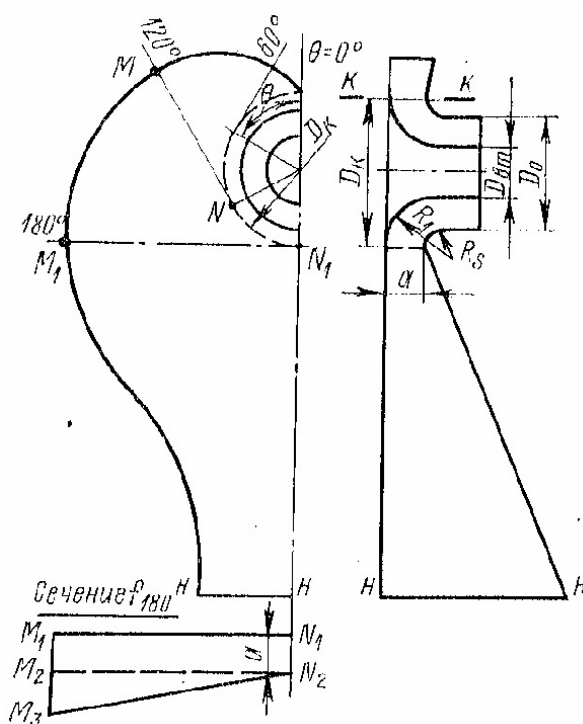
Схема и основные размеры входного патрубка промежуточной ступени
